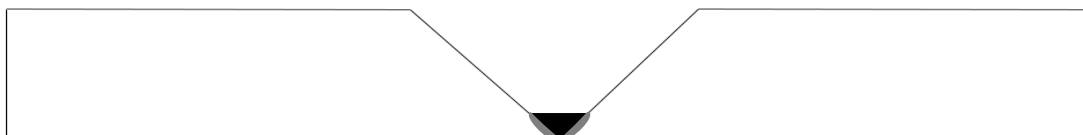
Esquema de soldadura semiautomática, a cinzento zona termicamente afetada
